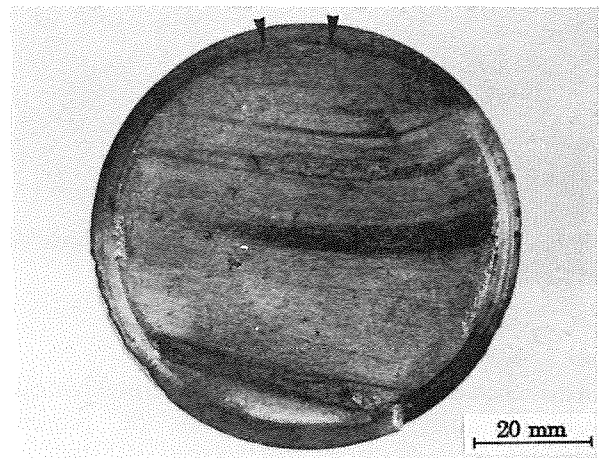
Aspecto de la superficie de fractura del lado de la parte roscada del tirante. Las flechas indican el inicio de la fractura.
